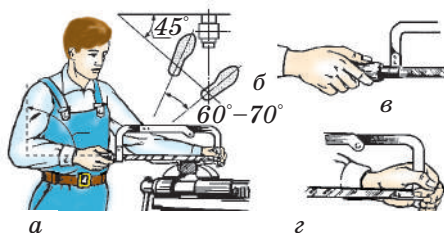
Прийоми різання ножівкою: а — розміщення корпусу й ножівки; б — розміщення ніг; в — розміщення правої руки; г — розміщення лівої руки
